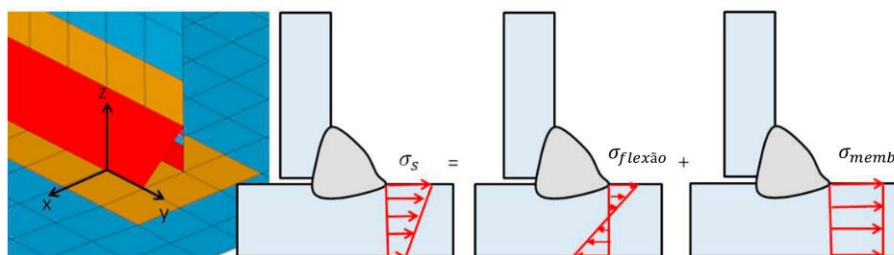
Distribuição dos esforços de membrana e flexão num cordão de soldadura (adaptado de [69])
